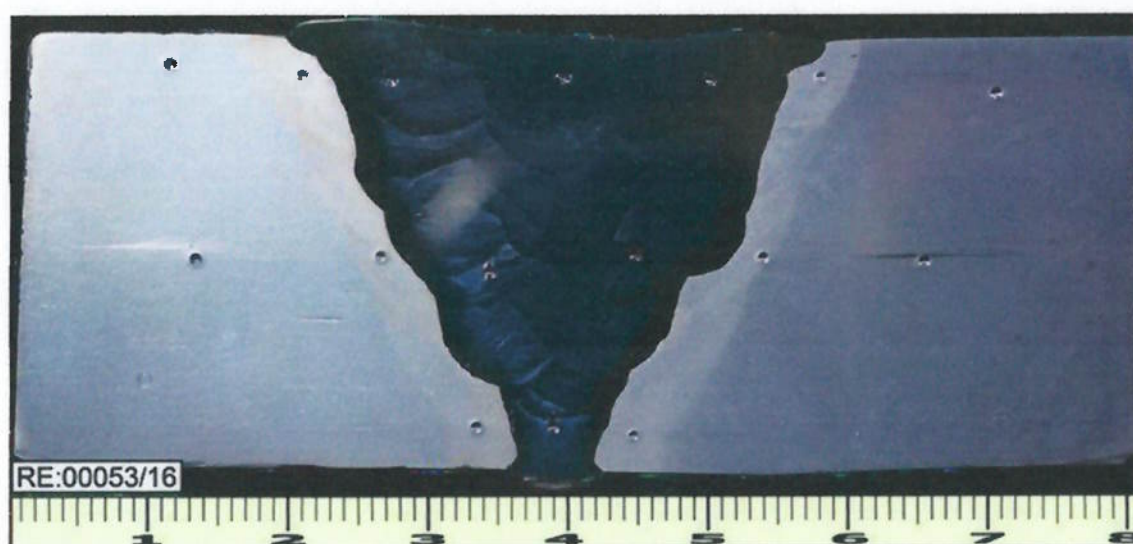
Macrografia da secção transversal do corpo de prova soldado com a amostra 625+Mg
